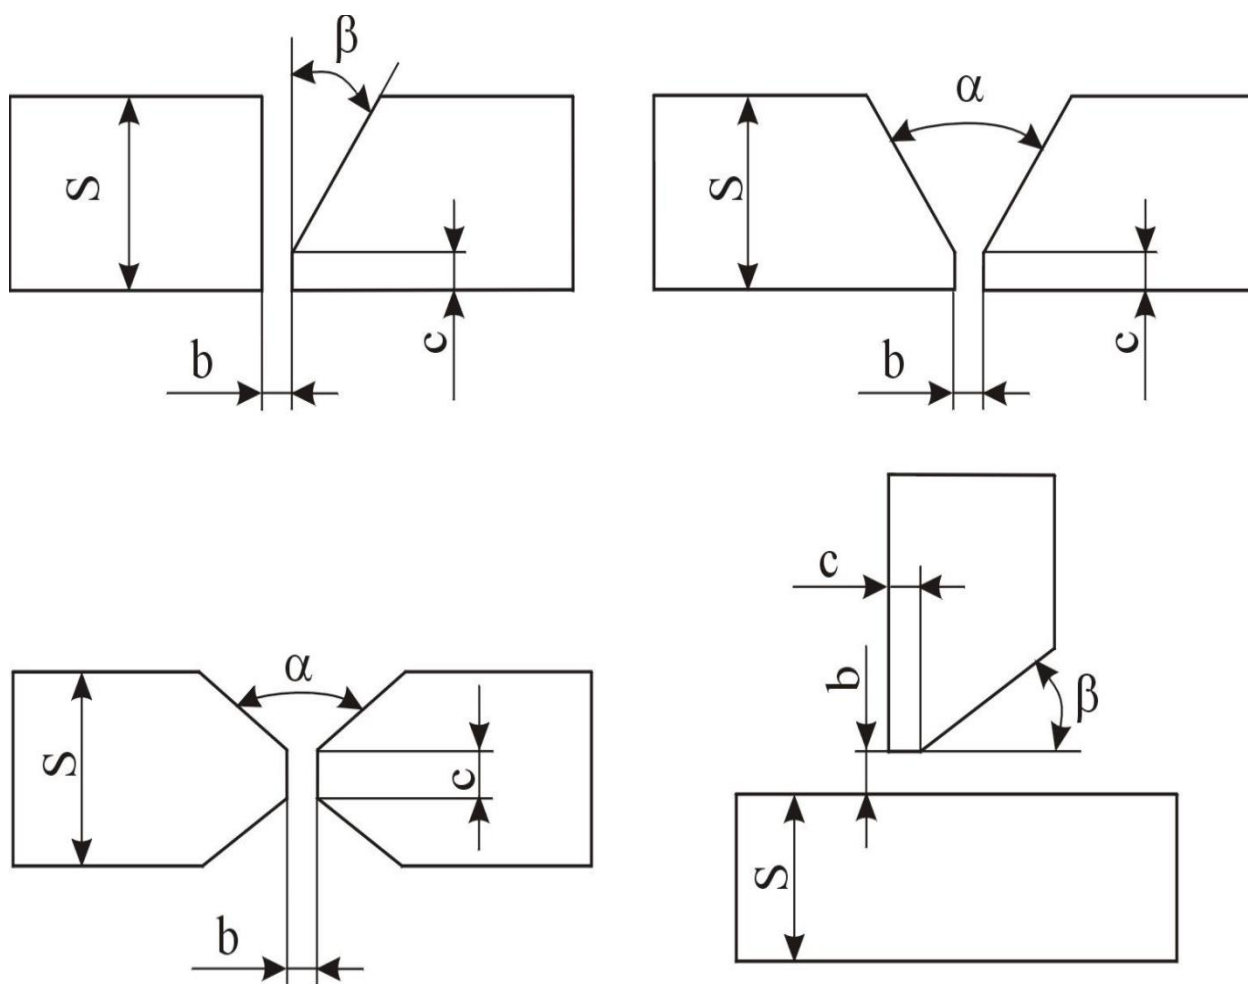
Конструктивные параметры разделки кромок и сборки под сварку: b - зазор; c - притупление кромки; β - угол скоса кромки; α - угол разделки кромок.
